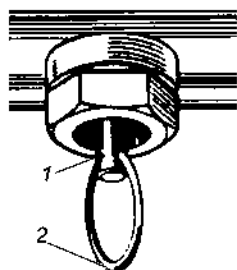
Устройство для слива конденсата автомобиля марки «КамАЗ»: 1 — шток; 2 — кольцо
